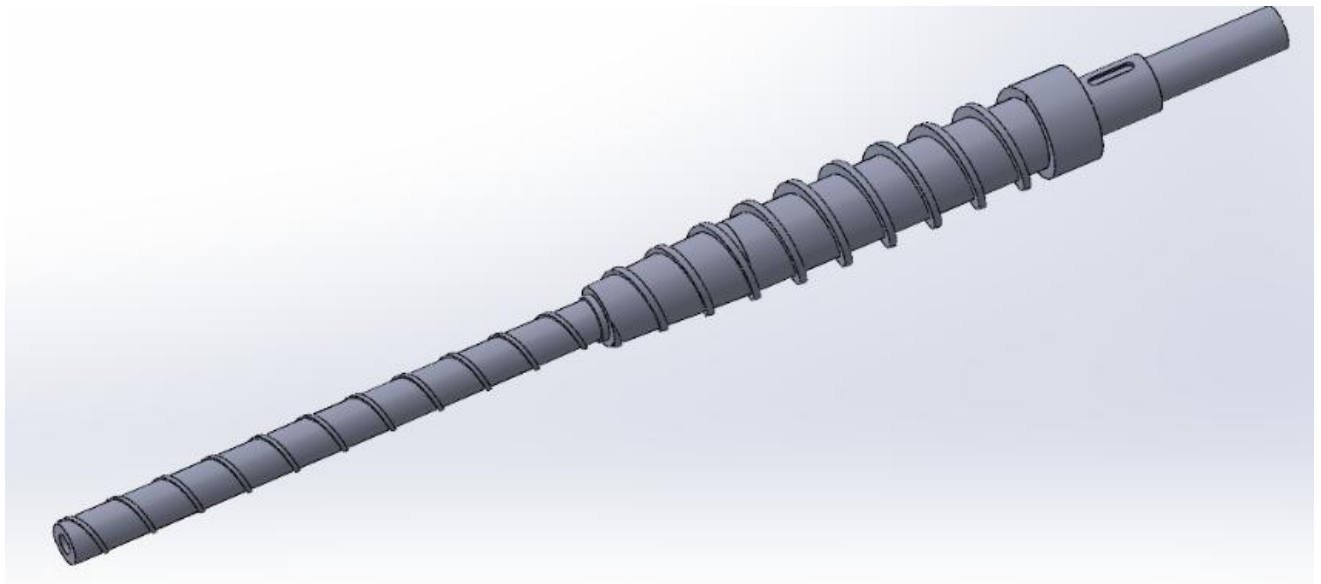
3D-модель модернізованого двосекційного черв'яка (SolidWorks)
